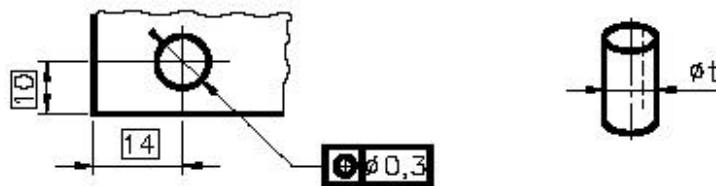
Tolerância de posição – especificação em desenho e interpretação.
